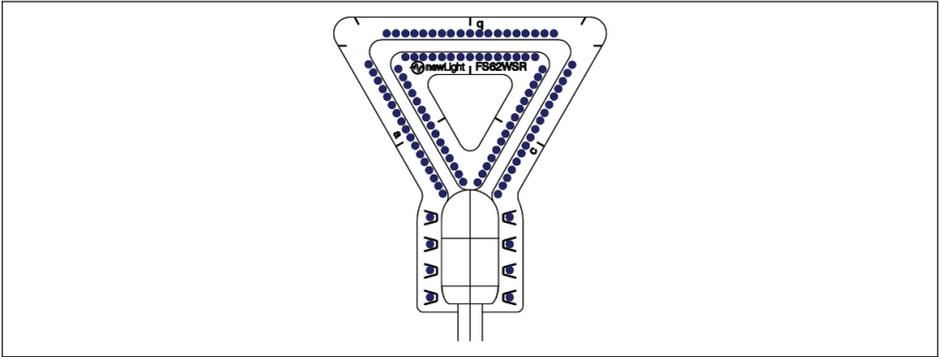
Schweißreihenfolge für die Rosette FS62WSR, Schritt 3
